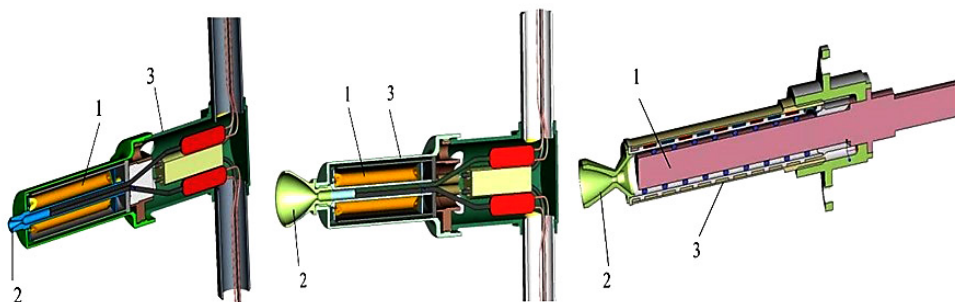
3D-модель электронагревного двигателя [6]: 1 — омический нагреватель; 2 — сопло камеры сгорания; 3 — корпус двигателя
